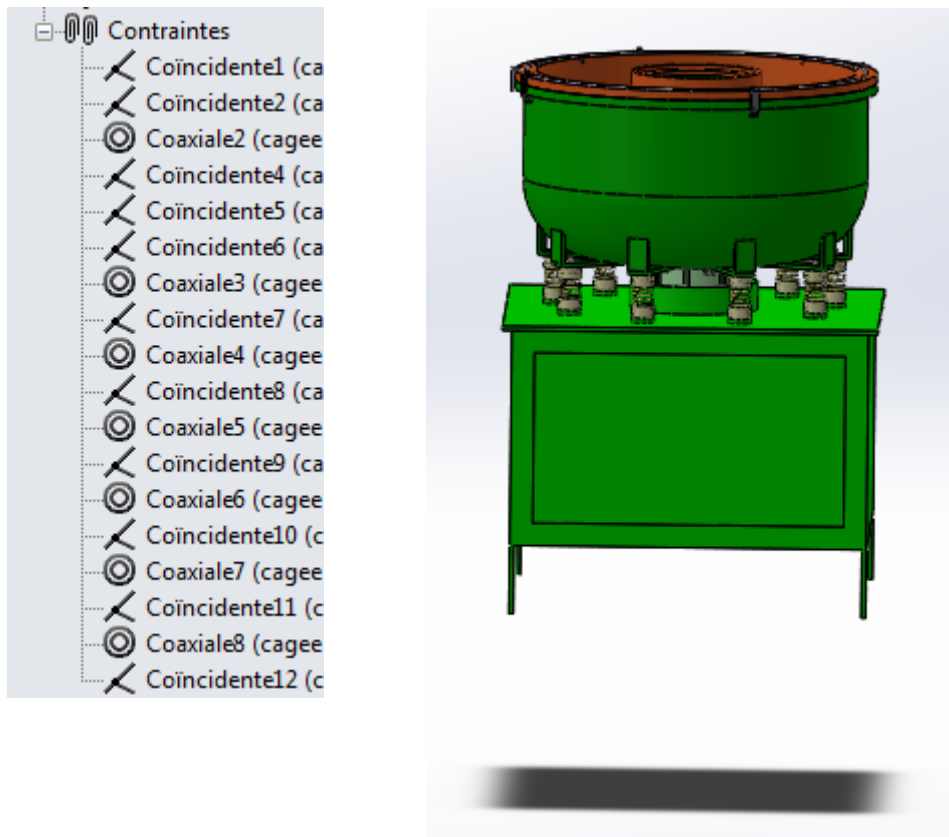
Les composantes du sous assemblage final dans une seule zone graphique
